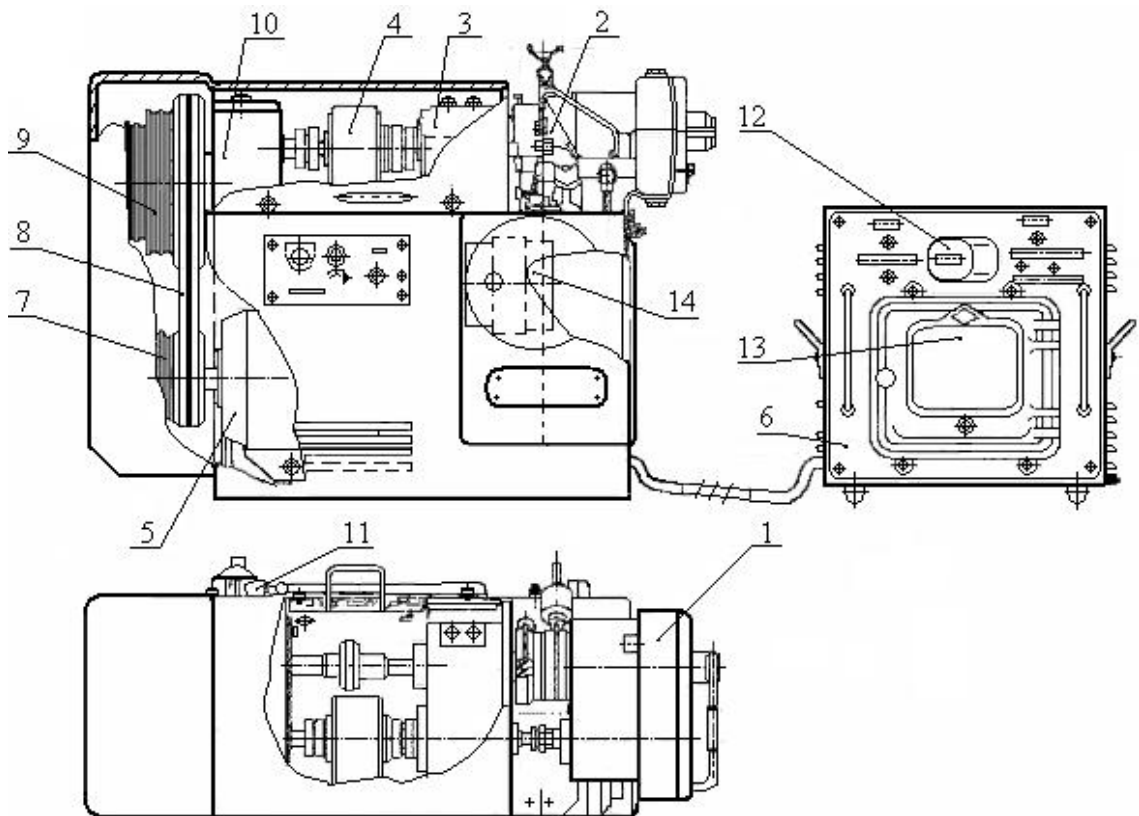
Загальний вигляд машини тертя СМЦ-2:
